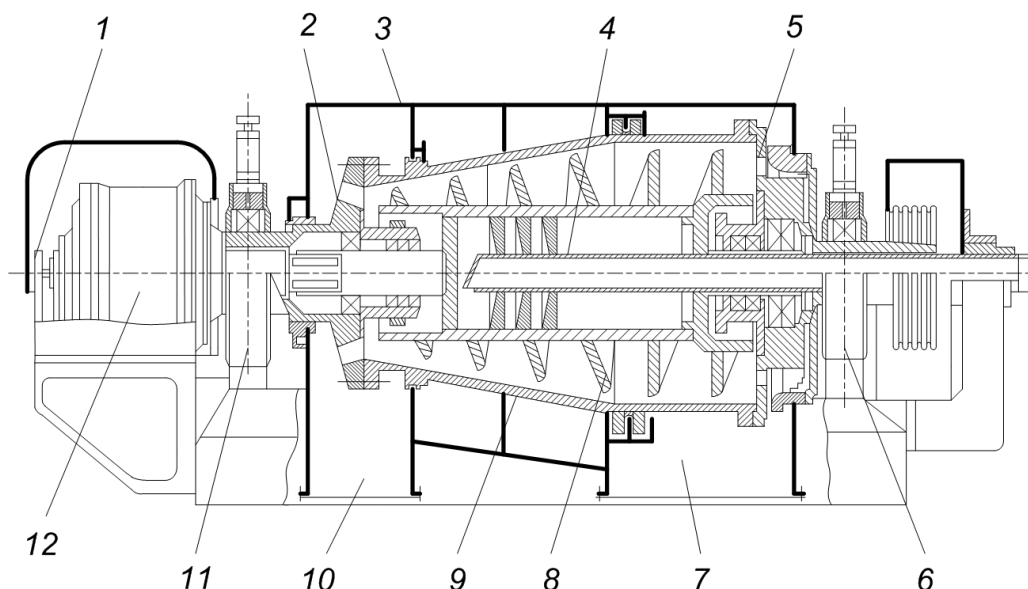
Схема центрифуги типа ОГШ: 1 – защитное устройство редуктора; 2, 5 – окна выгрузки осадка и слива фугата; 3 – кожух; 4 – питающая труба; 6, 11 – опоры; 7, 10 – штуцеры отвода фугата и выгрузки осадка; 8 – шнек; 9 – ротор; 12 – планетарный редуктор
